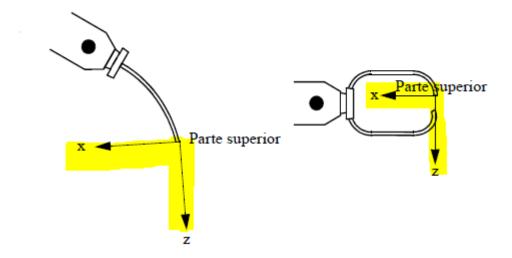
Sistema de coordenadas pistola de soldadura con arco (izquierda) y pistola soldadura por puntos (derecha).
